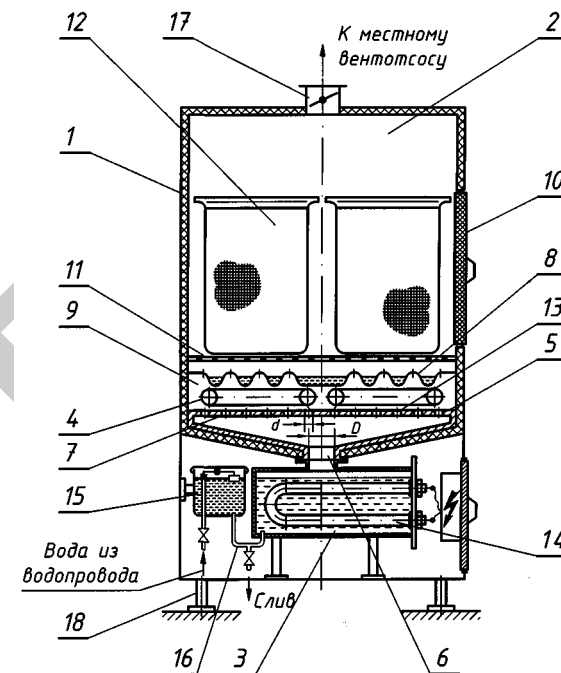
Принципиально-конструктивная схема пароварочного аппарата:
